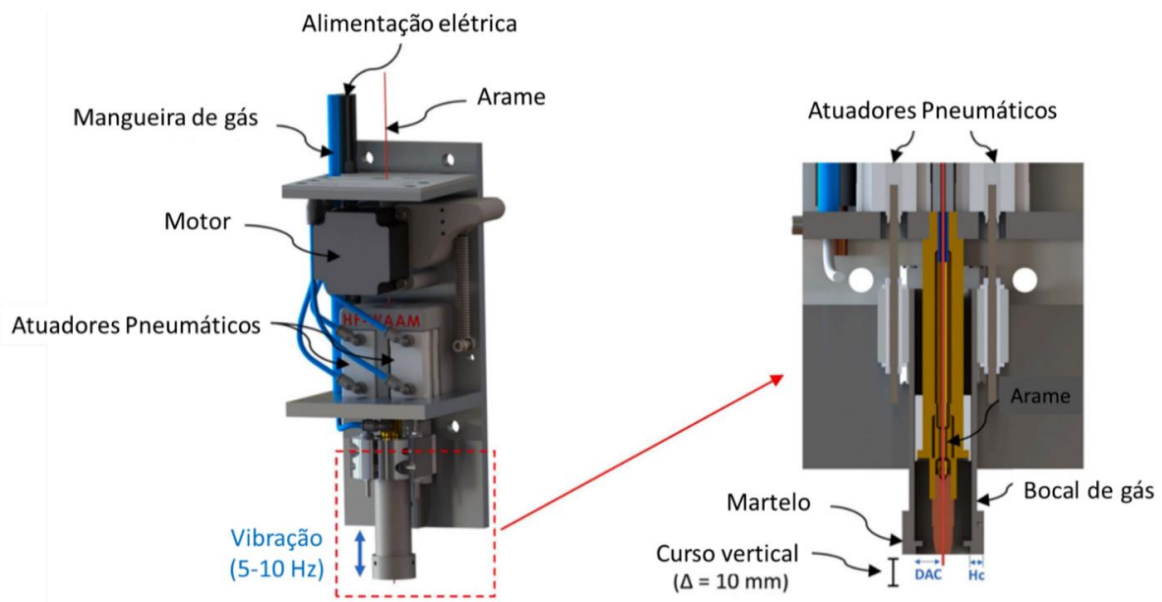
Representação esquemática dos equipamentos de soldadura e forjamento (adaptado de [42]).
